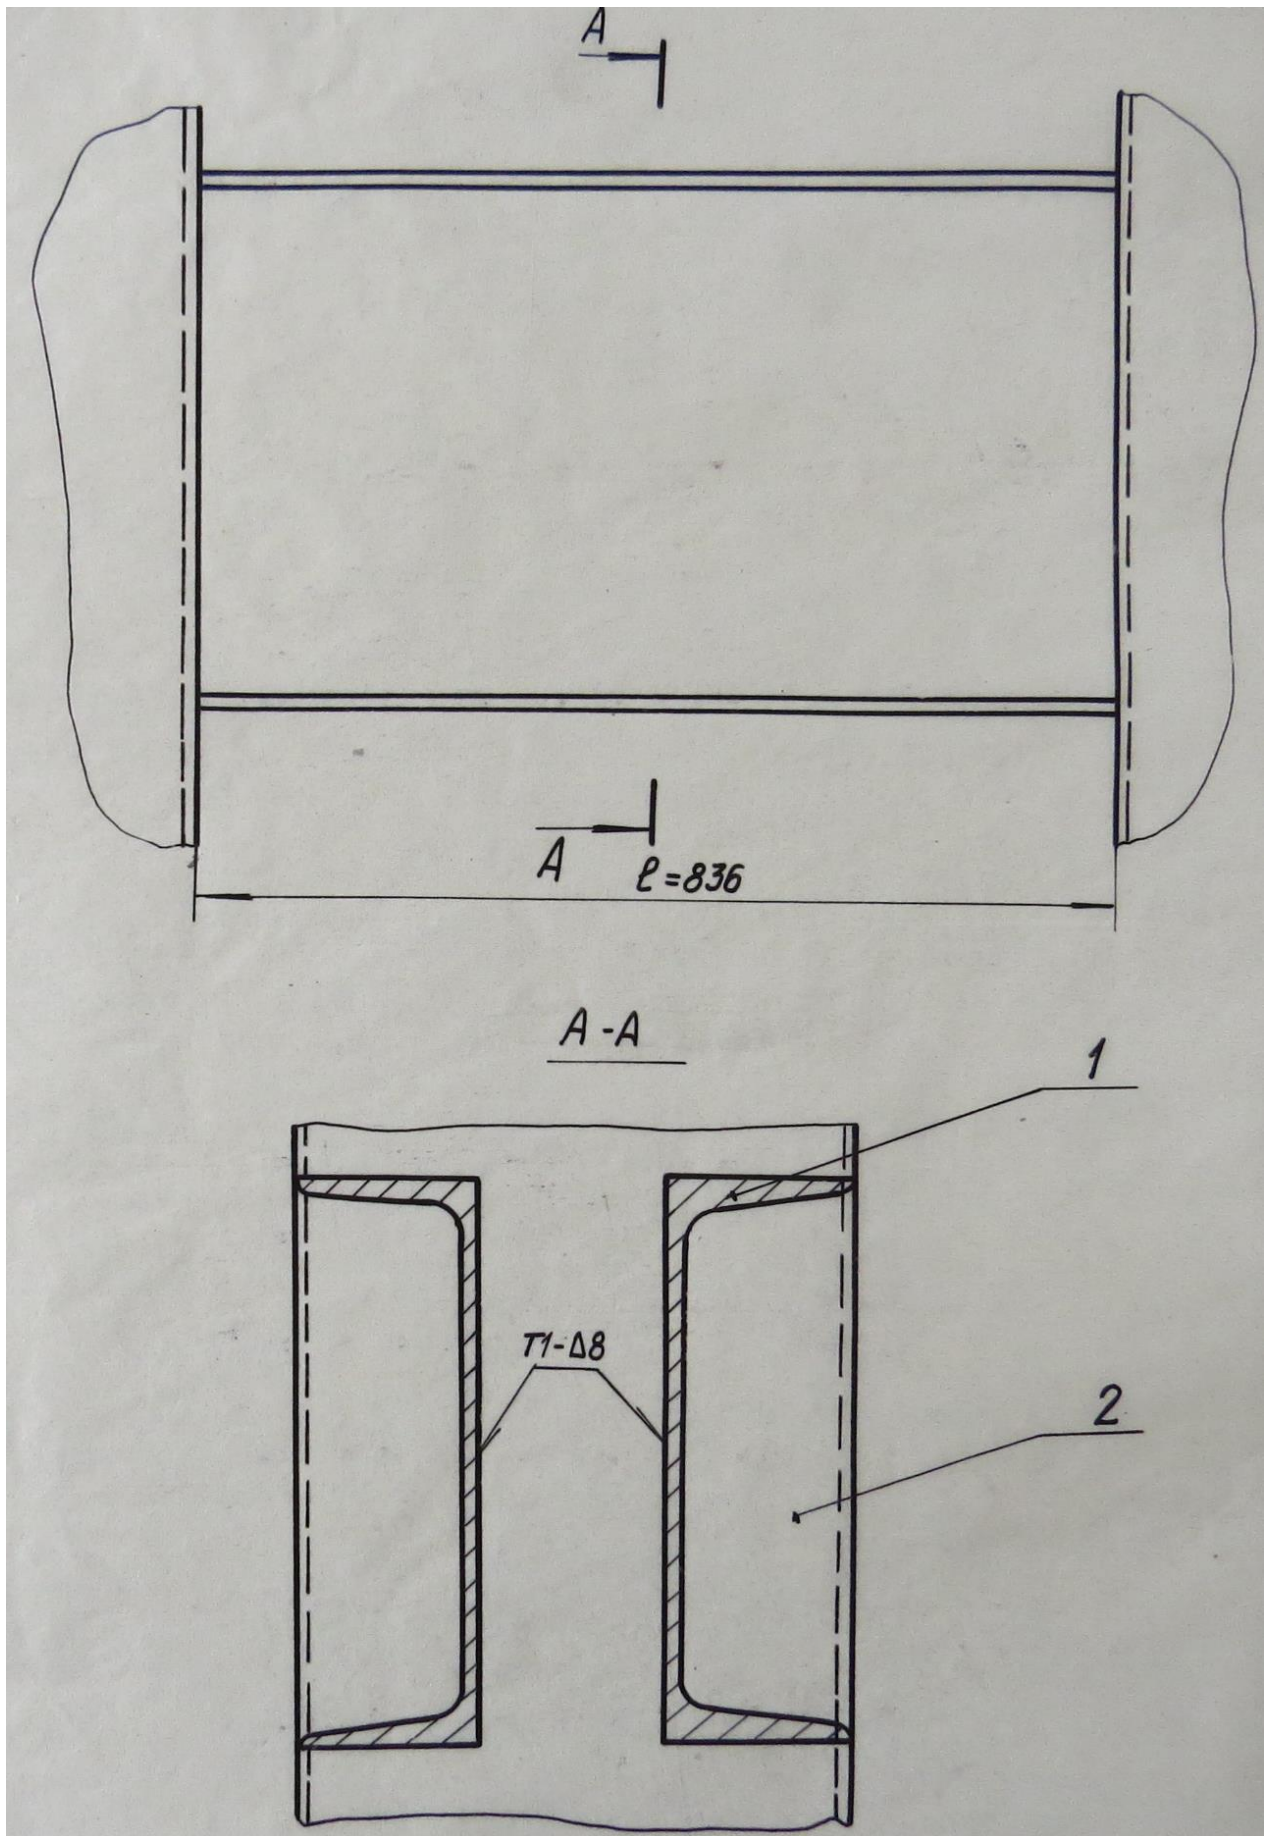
Конструкція зварювання балок з вертикальними стояками:
